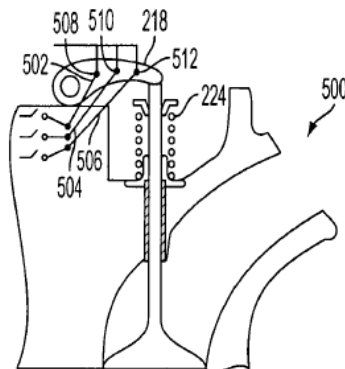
Conjunto de válvula acionado eletronicamente para um motor de combustão interna (Riley *et al.*, 2013).
